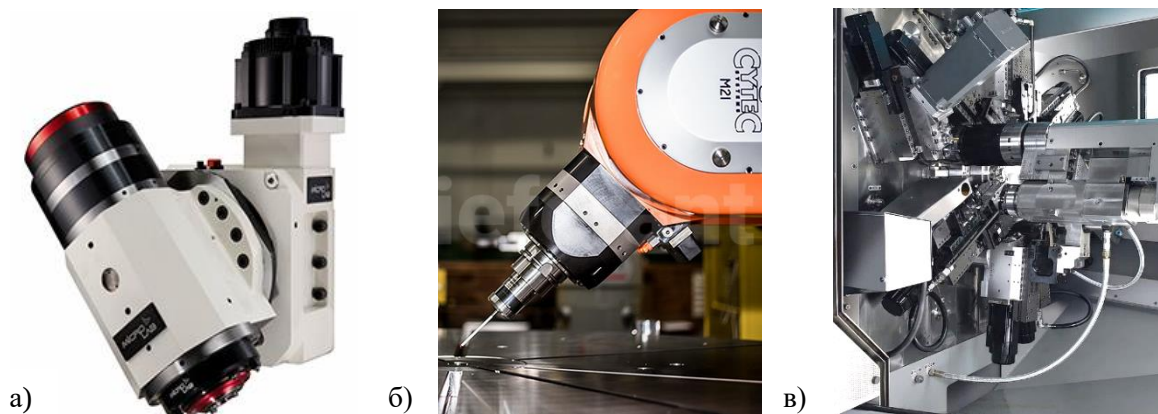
Сучасні інтелектуальні металообробні центри оснащені просторово адаптивними мотор-шпиндельними агрегатами: а) поворотний шпиндельний агрегат компанії MicroLab Precision Technology Co., Ltd., MicroLab; б) фрезерна шпиндельна головка CYTEC; в) багатошпиндельний автомат з ЧПУ MS40-8 компанії INDEX.
